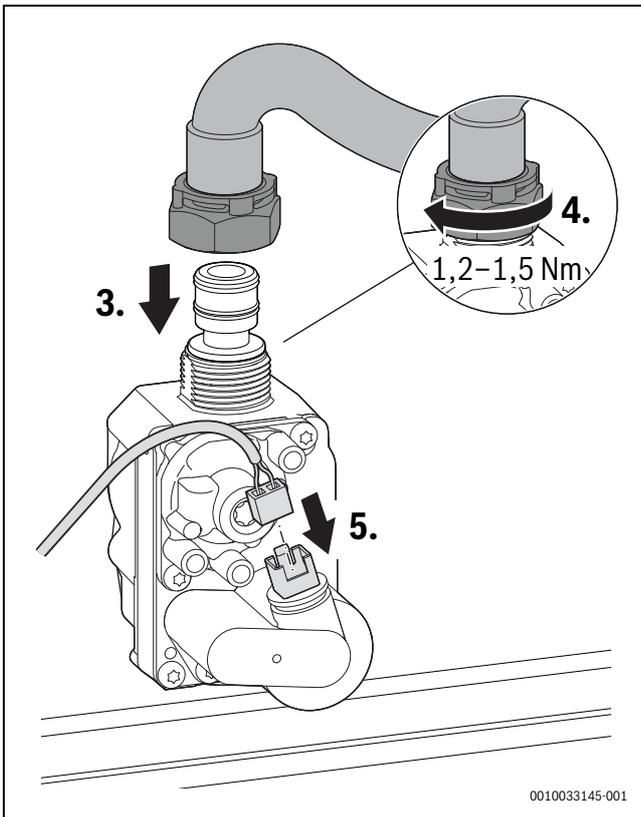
Collegamento di tubo flessibile del gas e connettore – Rispettare la coppia di serraggio
